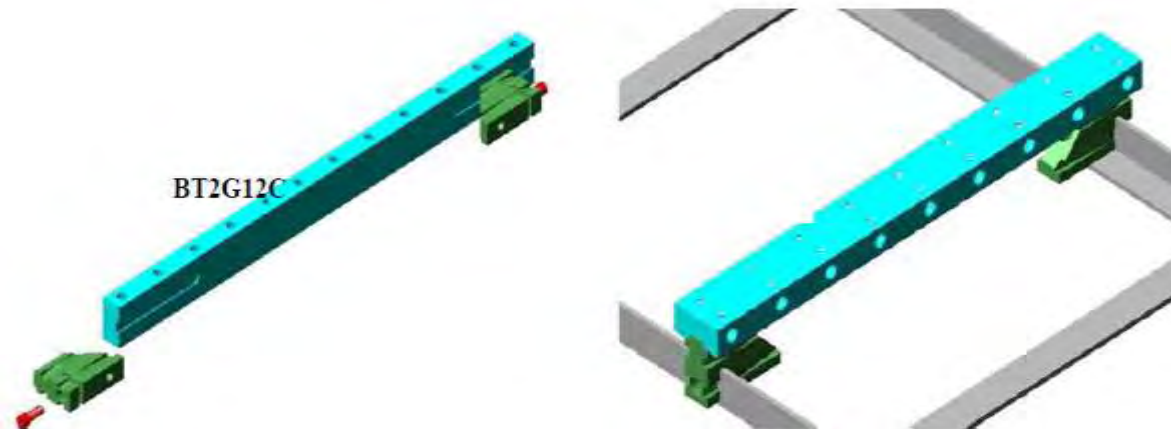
Barras de acero galvanizado BT2G12C con aisladores deslizables.
